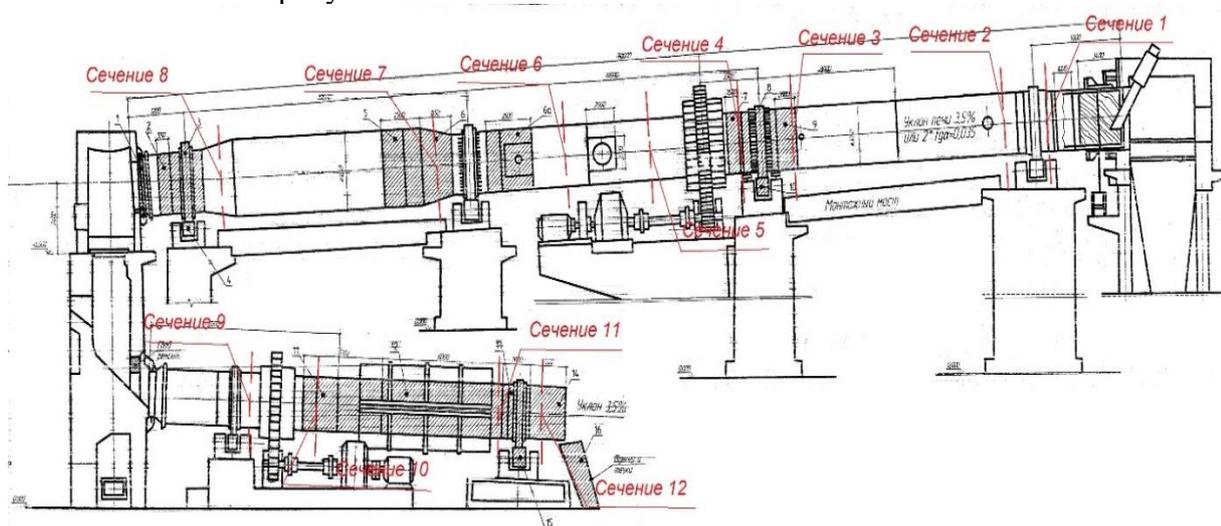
Расположение сечений замера толщины и твердости металла элементов вращающейся печи
